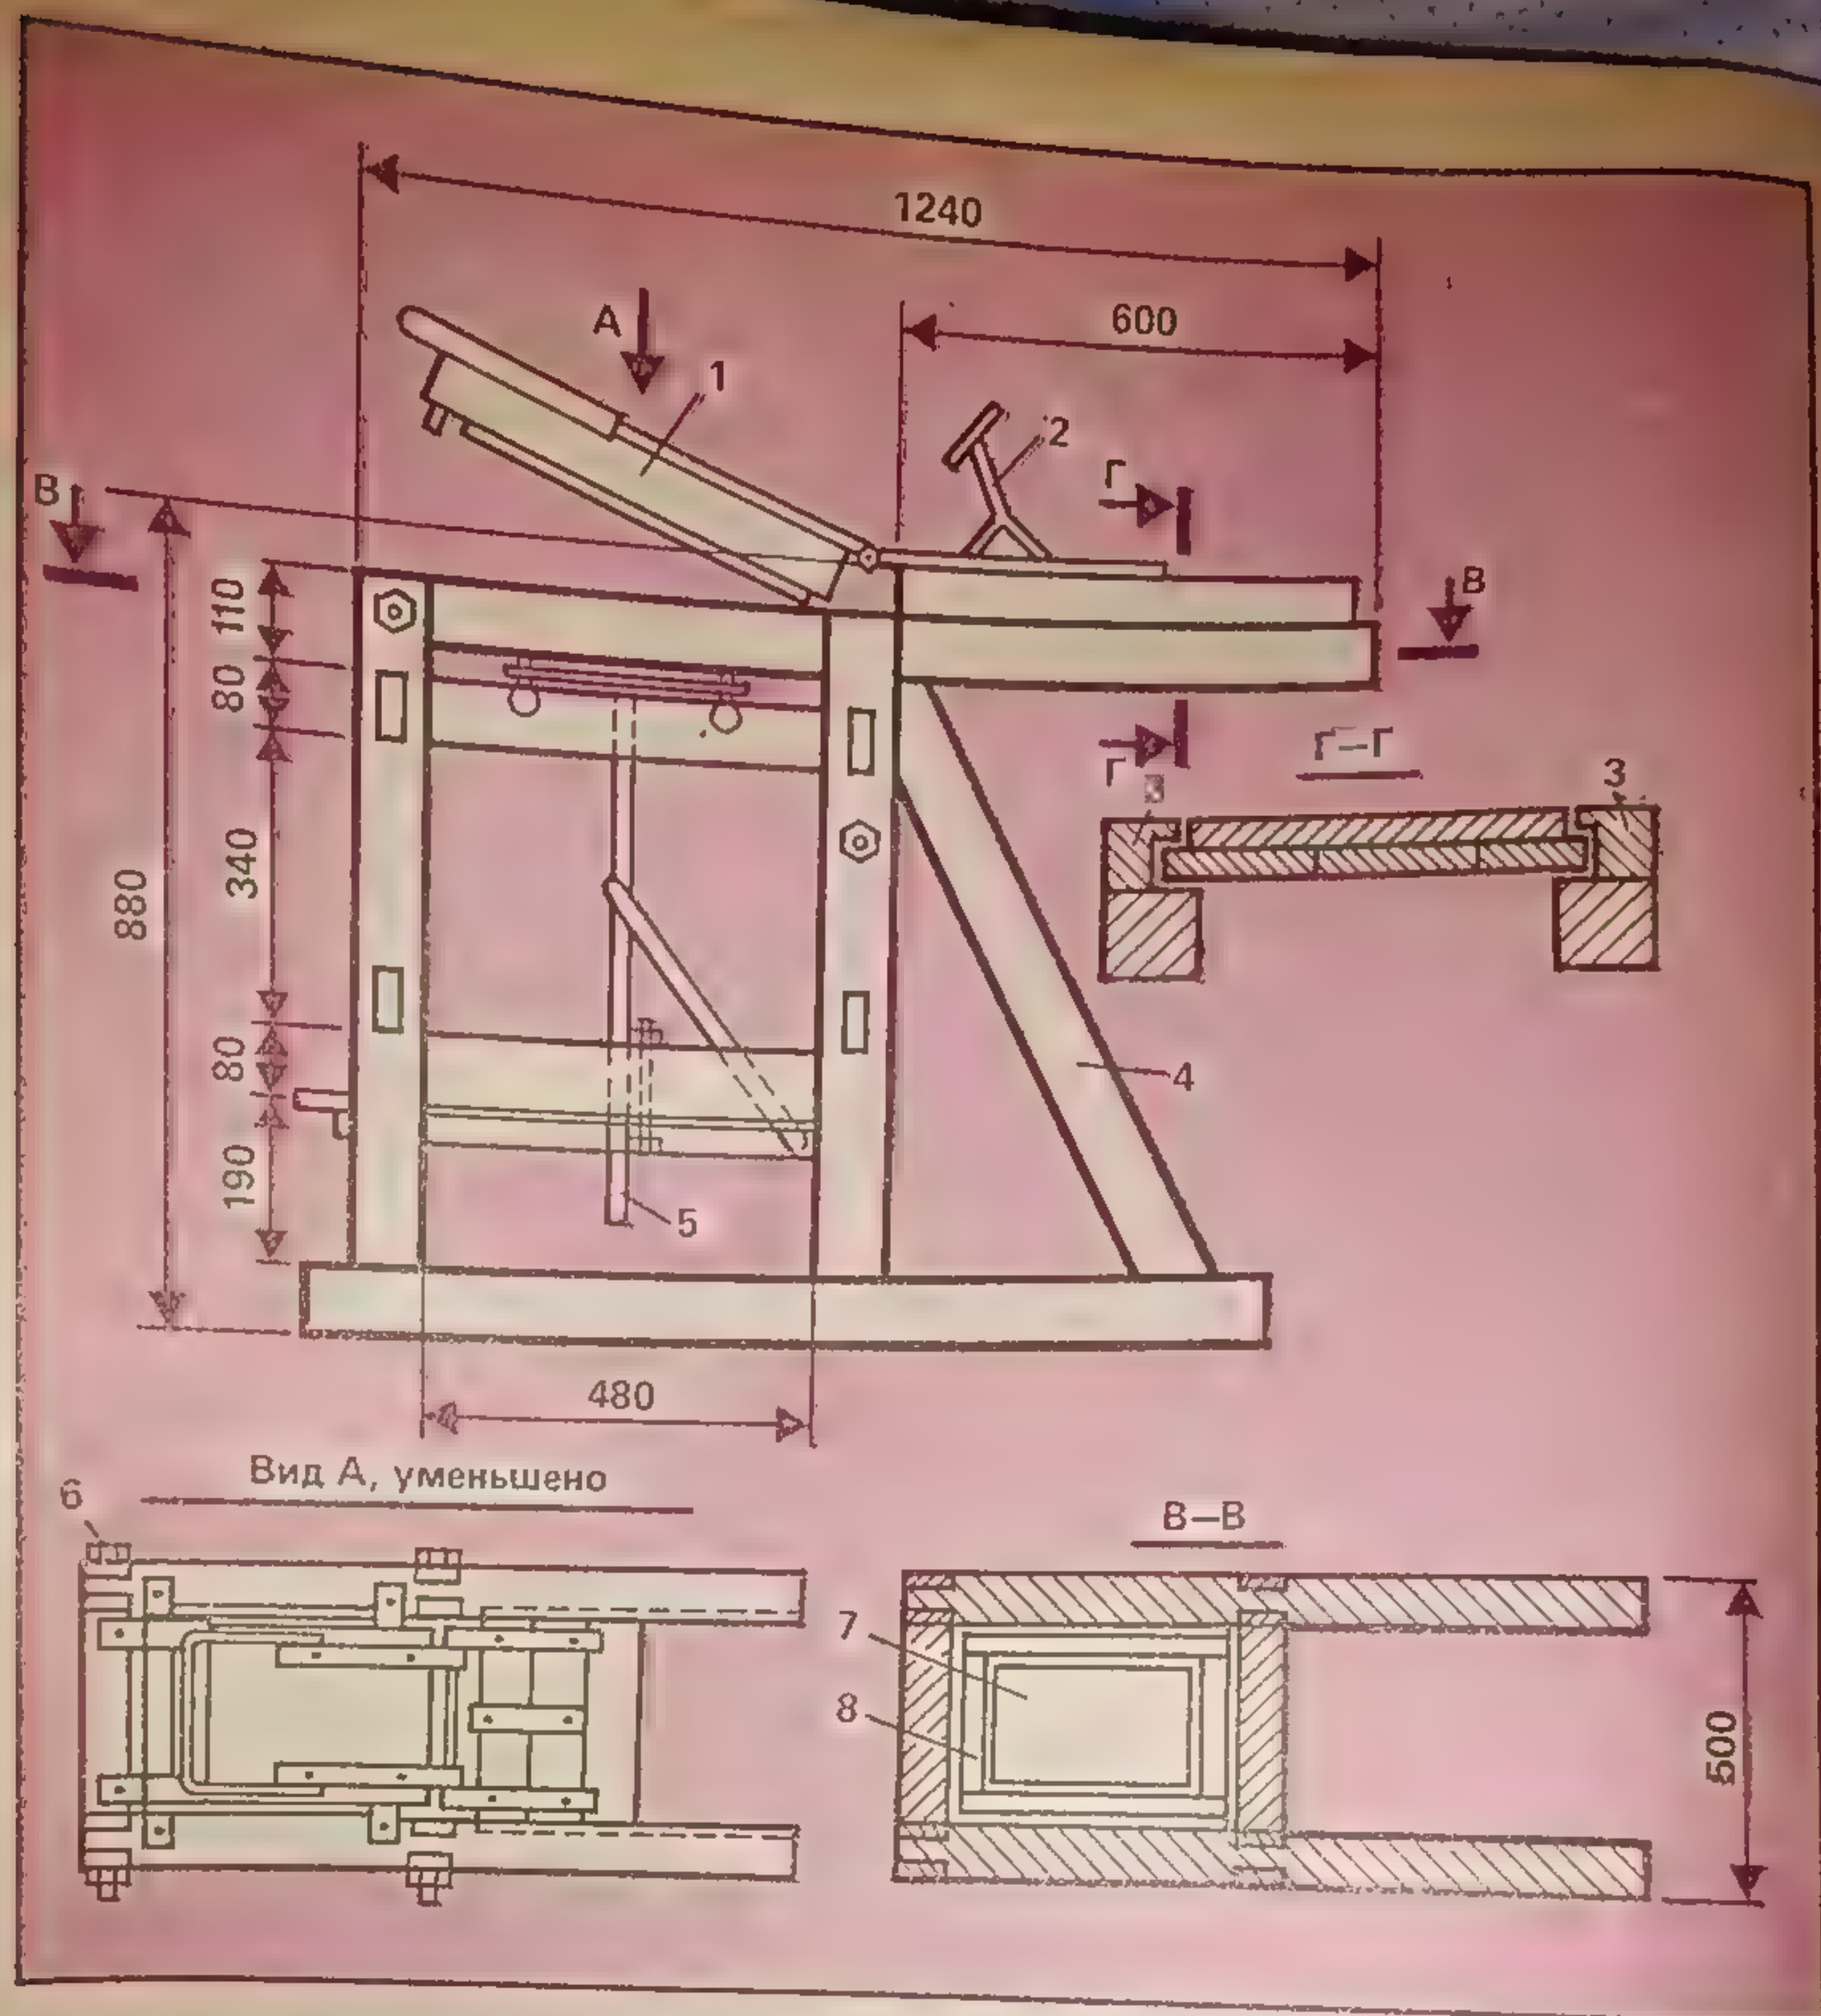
Деревянный формовочный станок: 1 — пуансон; 2 — опора; 3 — брус-ограничитель, 4 — станина; 5 — выталкивающий механизм; 6 — стяжная шпилька; 7 — матрица; 8 — форма
